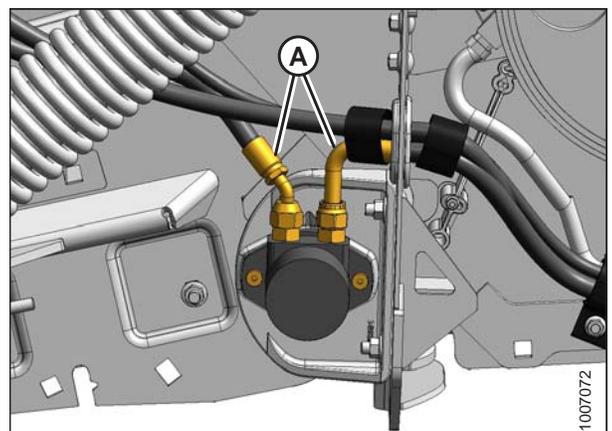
Motor hidráulico trasero; lado izquierdo
